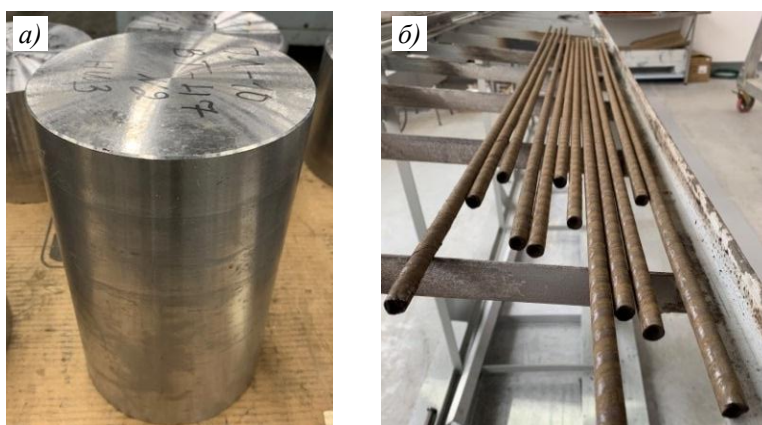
Внешний вид слитка (а) и катаного прутка (б) из сплава ВТ47
